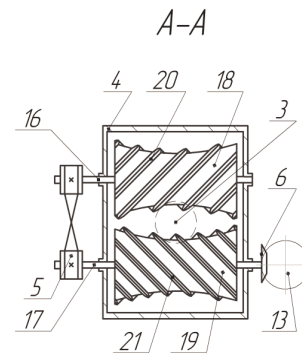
Общий вид устройства для извлечения ядер из кедровых орехов
